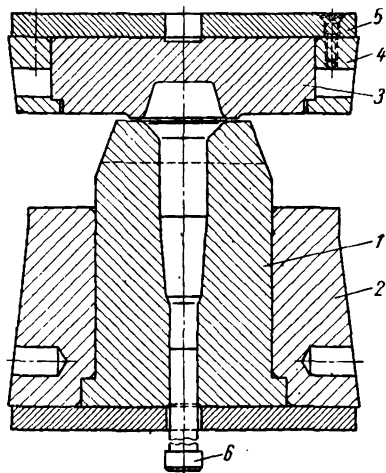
Вставка окончательного ручья: 1 — матрица; 2 — державка матрицы; 3 — формующий пуансон; 4 — державка пуансона; 5 — подкладка; 6 — выталкиватель
